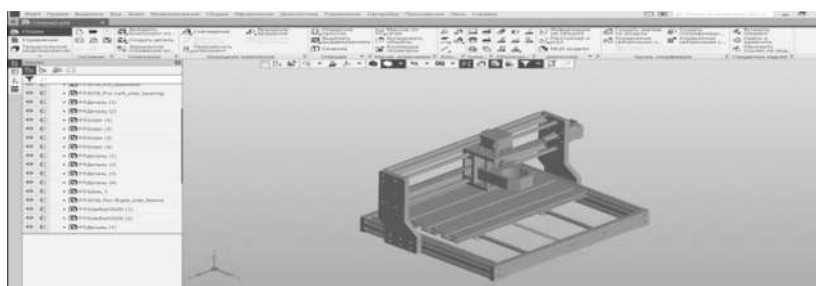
3D модель лабораторного трехкоординатного ударно-точечного маркировочного станка с ЧПУ
